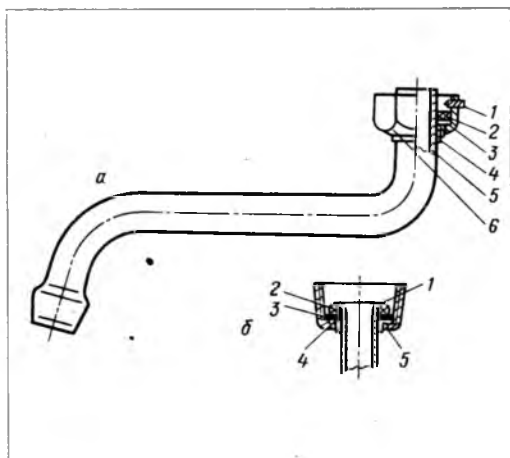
Излив со стопором: а — конструкция излива (1 — стопорный винт; 2 — прокладка; 3 — шайба латунная; 4 — кольцо; 5 — трубка; 6 — накладная гайка); б — временный ремонт излива развальцовкой трубки (1 — развальцованная трубка; 2 — лен; 3 — прокладка; 4 — кольцо; 5 — накладная гайка)
